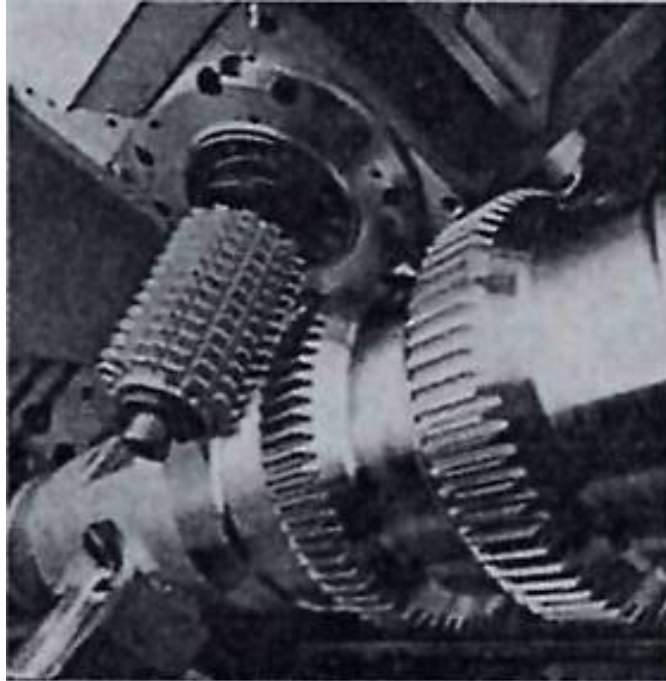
Установка червячной фрезы в револьверной головке токарного многоцелевого станка Millturn фирмы "WFL Technologies GmbH&Co.KG"
